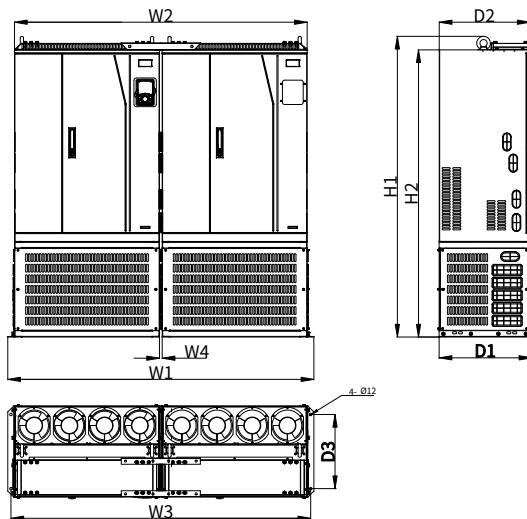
660V 800~3600kW 并机外形及安装尺寸
